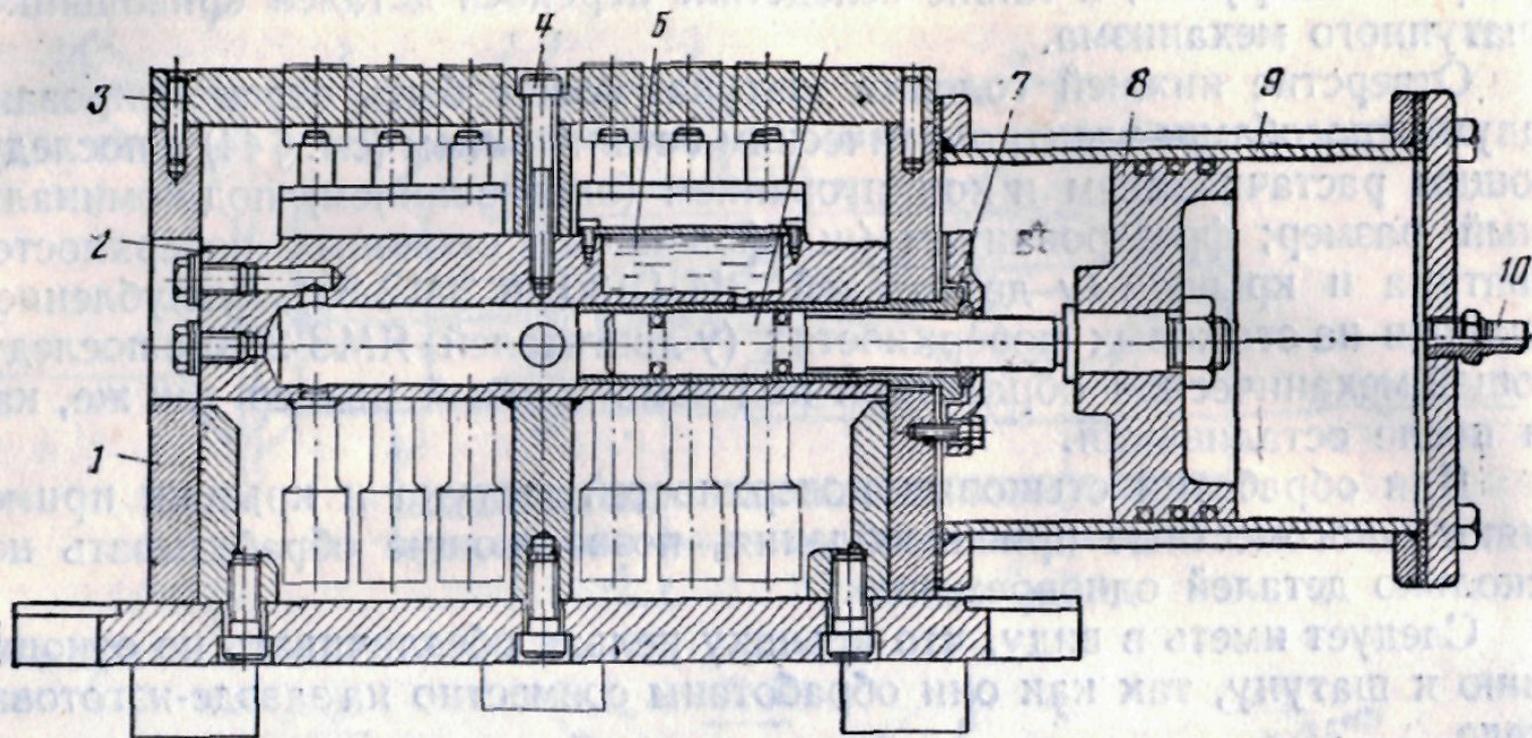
Приспособление для фрезерования стыковых поверхностей шатунов и их крышек
